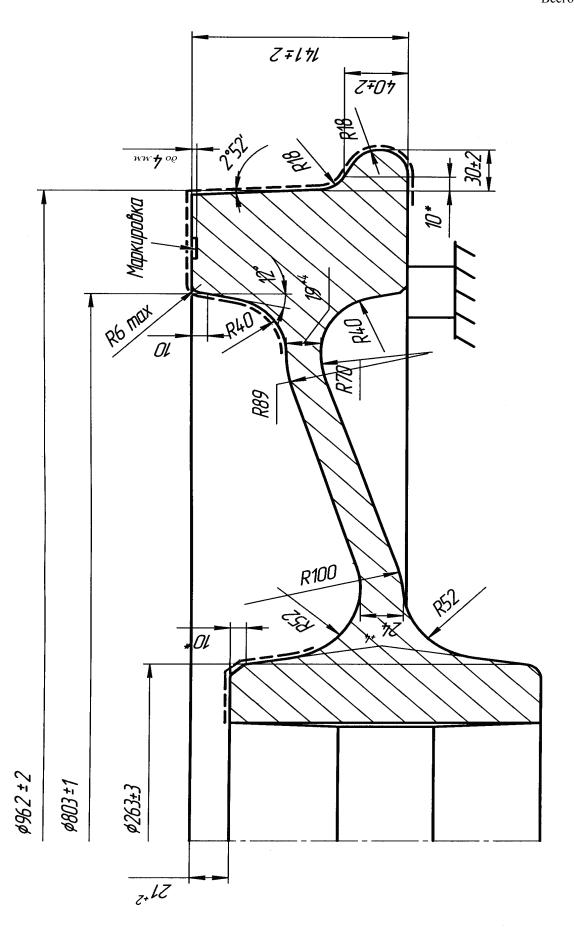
Колесо Ø962 мм с черновой механической обработкой, для Ø957 мм по чертежу № КР-0048-15. Масса колеса 450кг
